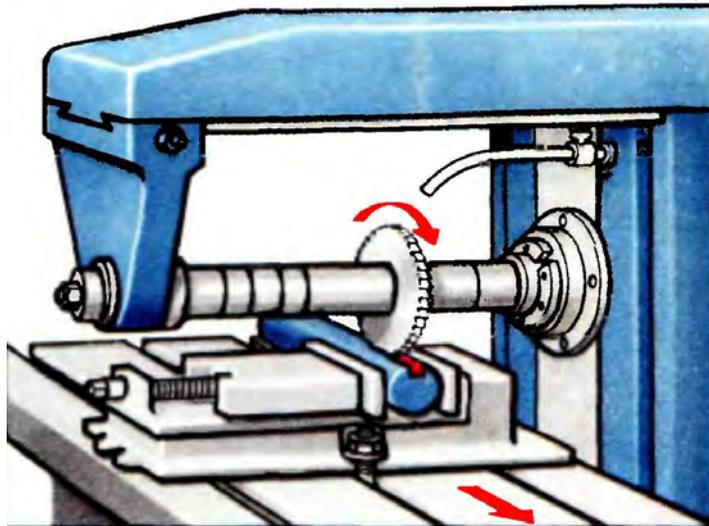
Фрезерование сквозного шпоночного паза дисковой фрезой
